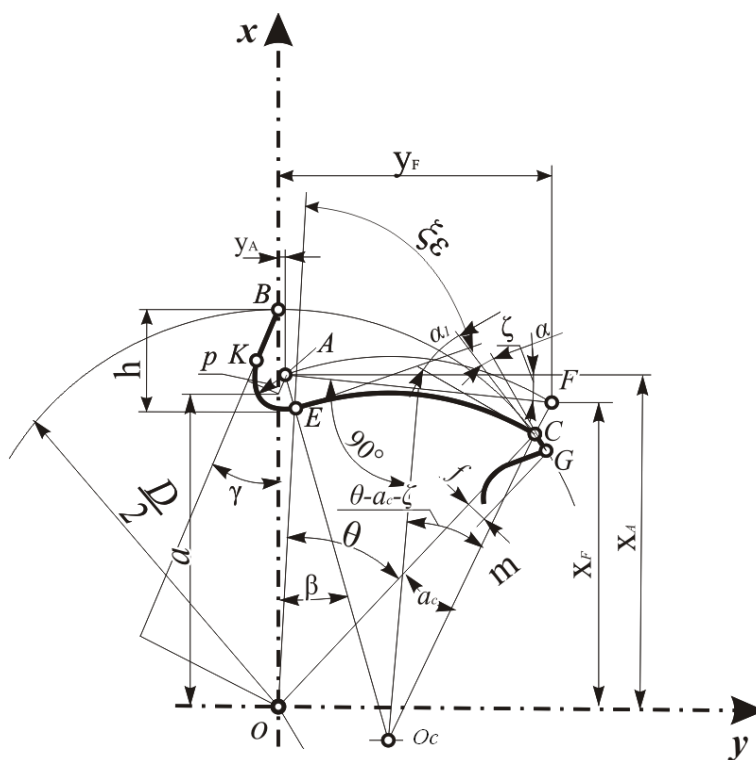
Форма профиля стружечной канавки концевой фрезы и его основные параметры
